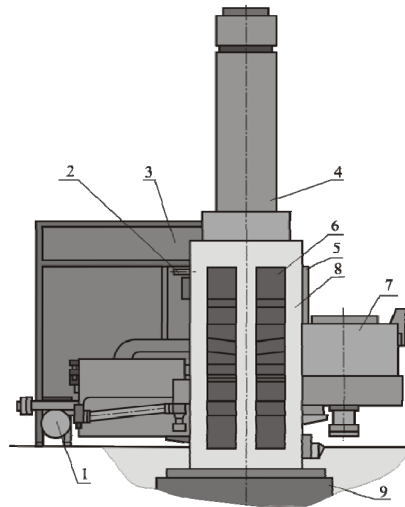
Загальний вигляд модернізованого обладнання моделі Т-1324М: 1 – дозатор; 2 – розводка; 3 – блок приводу; 4 – машина; 5 – електрошкафа; 6 – пневмоударний блок; 7 – технологічний блок; 8 – щока; 9 – фундамент
